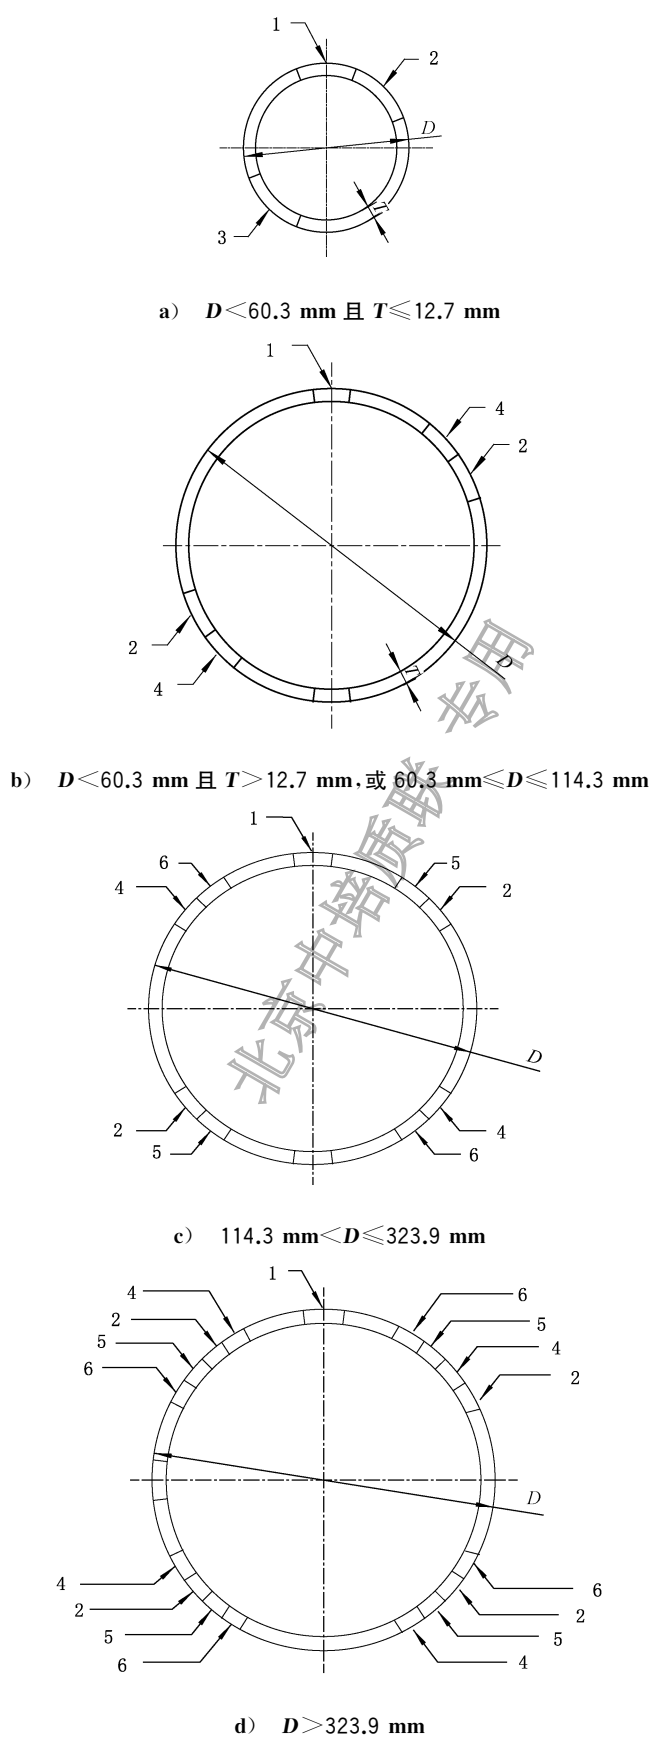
对接接头焊接工艺评定试验的试样位置
